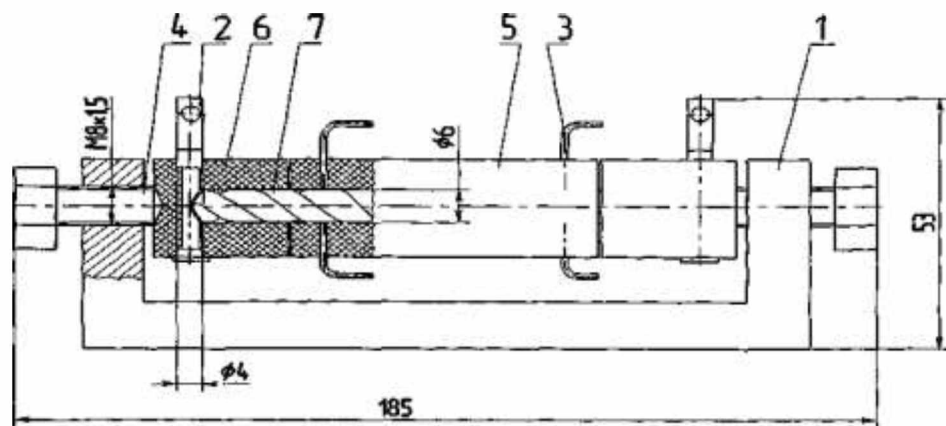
Пристрій для вимірювання омичного опору свердла
